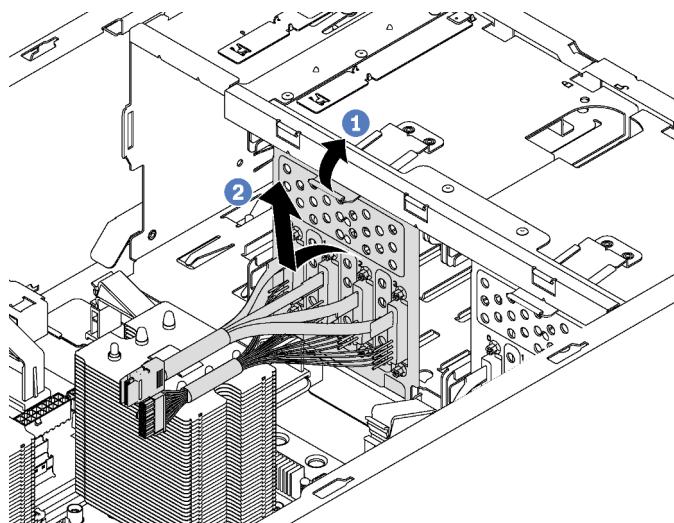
Retrait de la plaque arrière d'unité à remplacement standard
